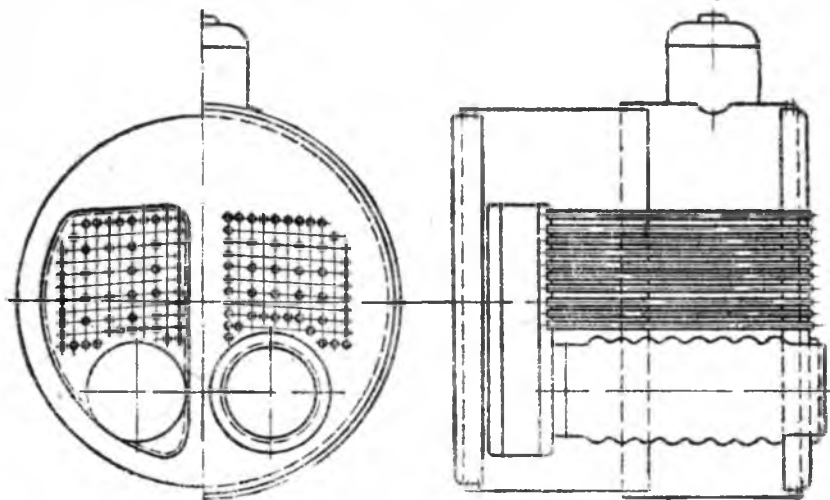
Советский сварной однопочный одинарный оборотный котел.
